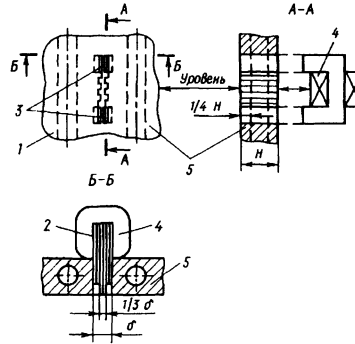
Индуктивный датчик, размещенный в ползуне: 1 — ползун; 2 — магнитопровод; 3 — канал водоохлаждения; 4 — намагничивающая катушка; 5 — формирующая поверхность ползуна
